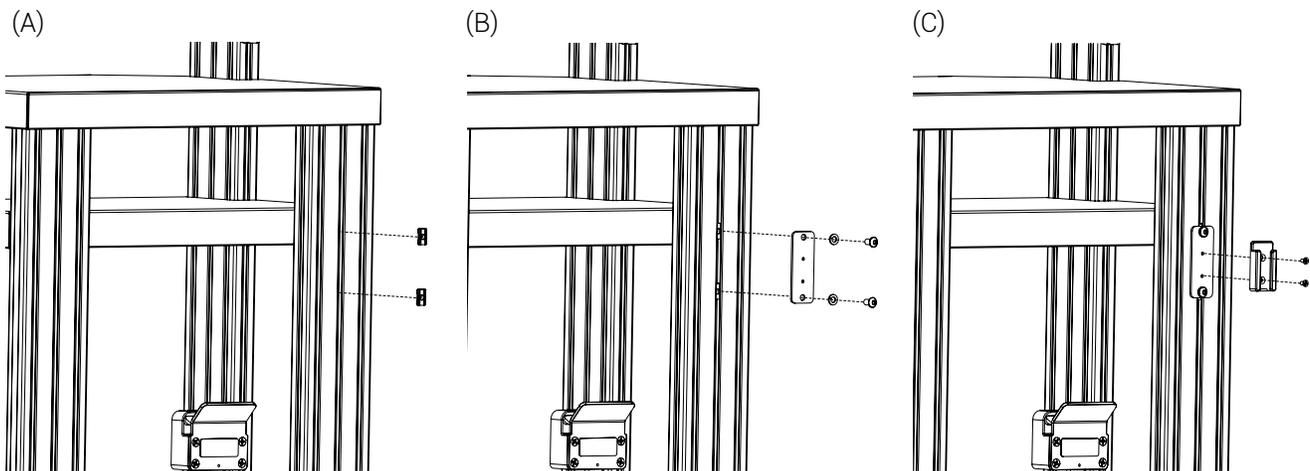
Pièces d'assemblage de la plaque-support pour bocal d'aspiration Serres
